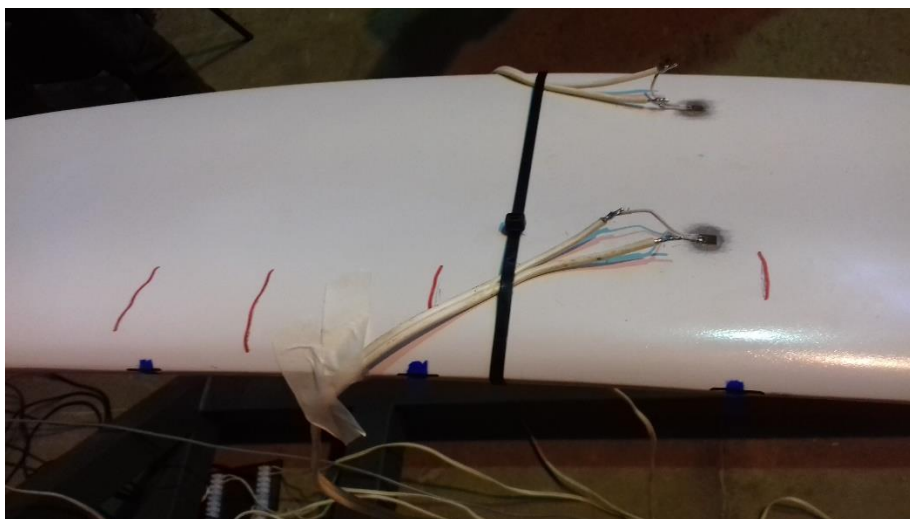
Local das fissuras no ensaio 1.
